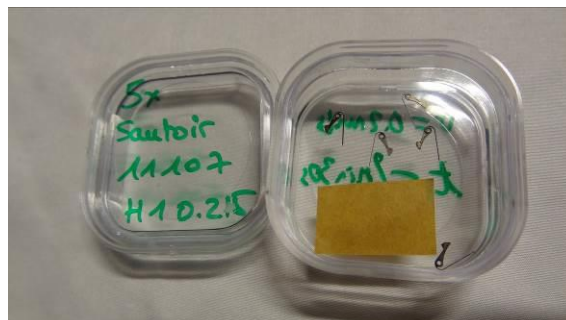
Vue macroscopique, $v=0.2$ mm/s.
